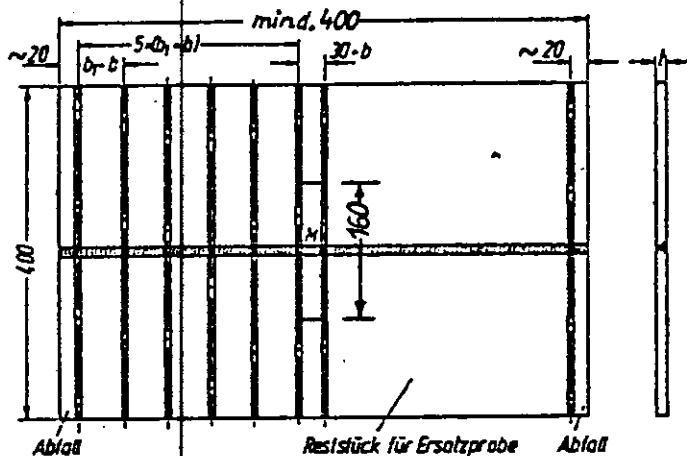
Schweißprobe 1 und Aufteilung für Zugproben und Makroschliff
